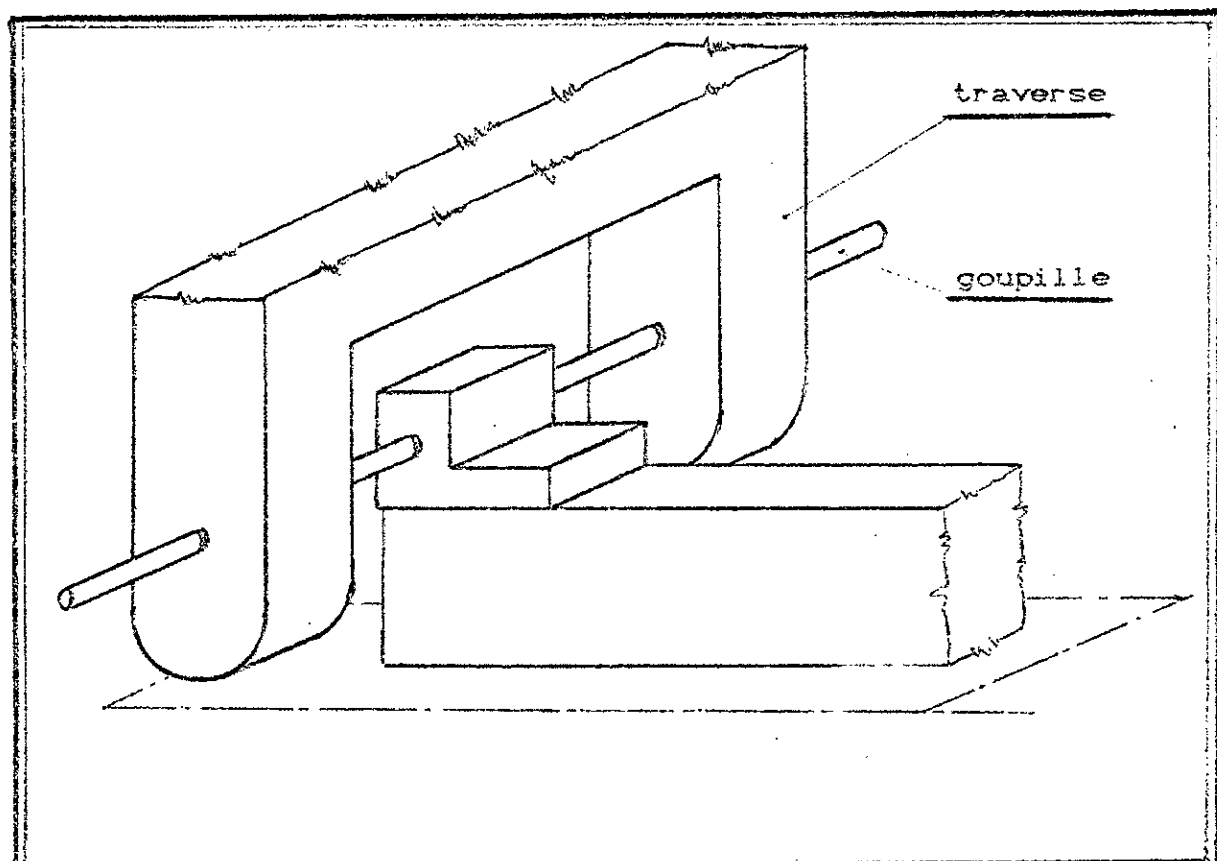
MONTAGE DE LA D.P.E SUR LA MACHINE
